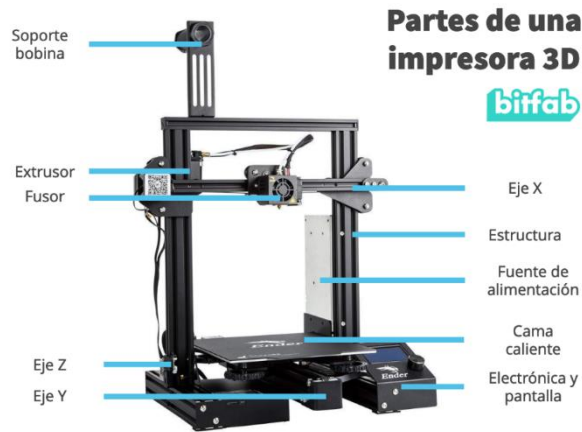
Diseño junto con sus partes se compone una impresora 3D de tipo FDM
